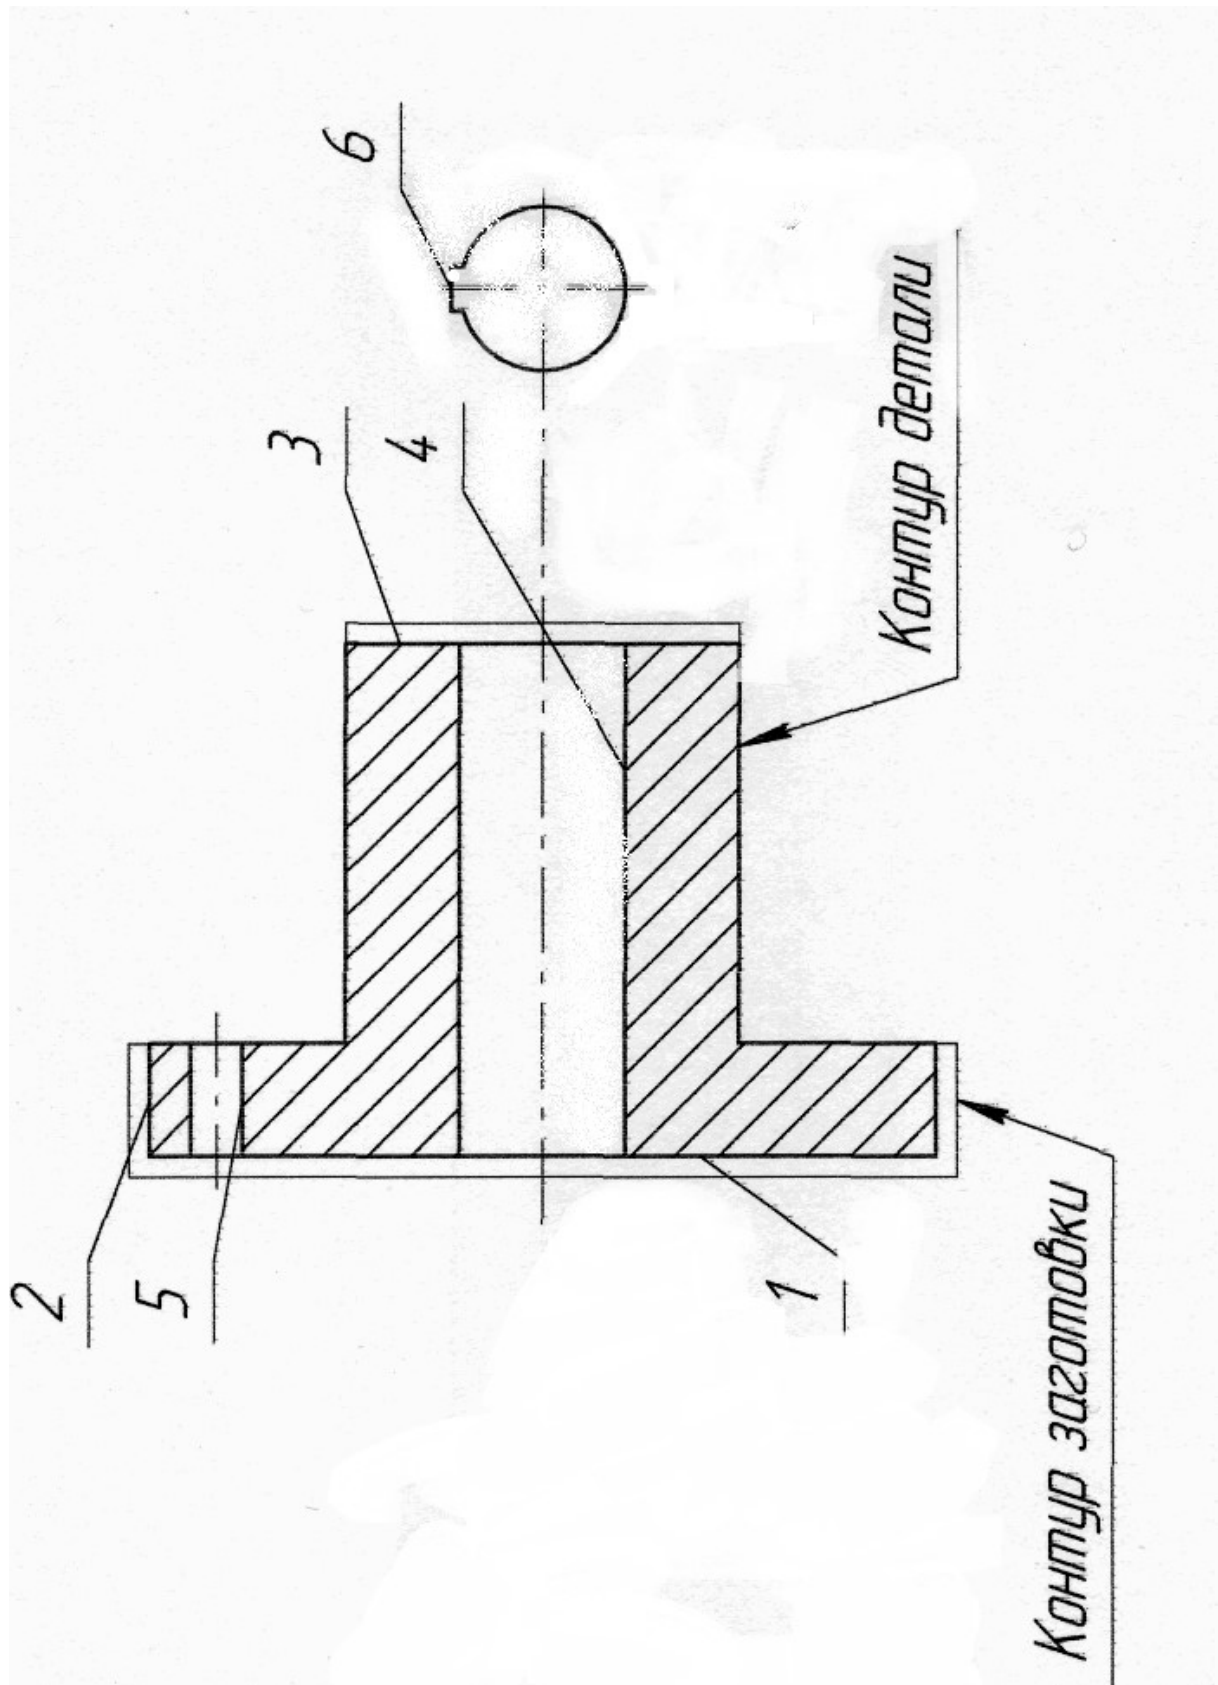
Пример обозначения обрабатываемых поверхностей заготовки
